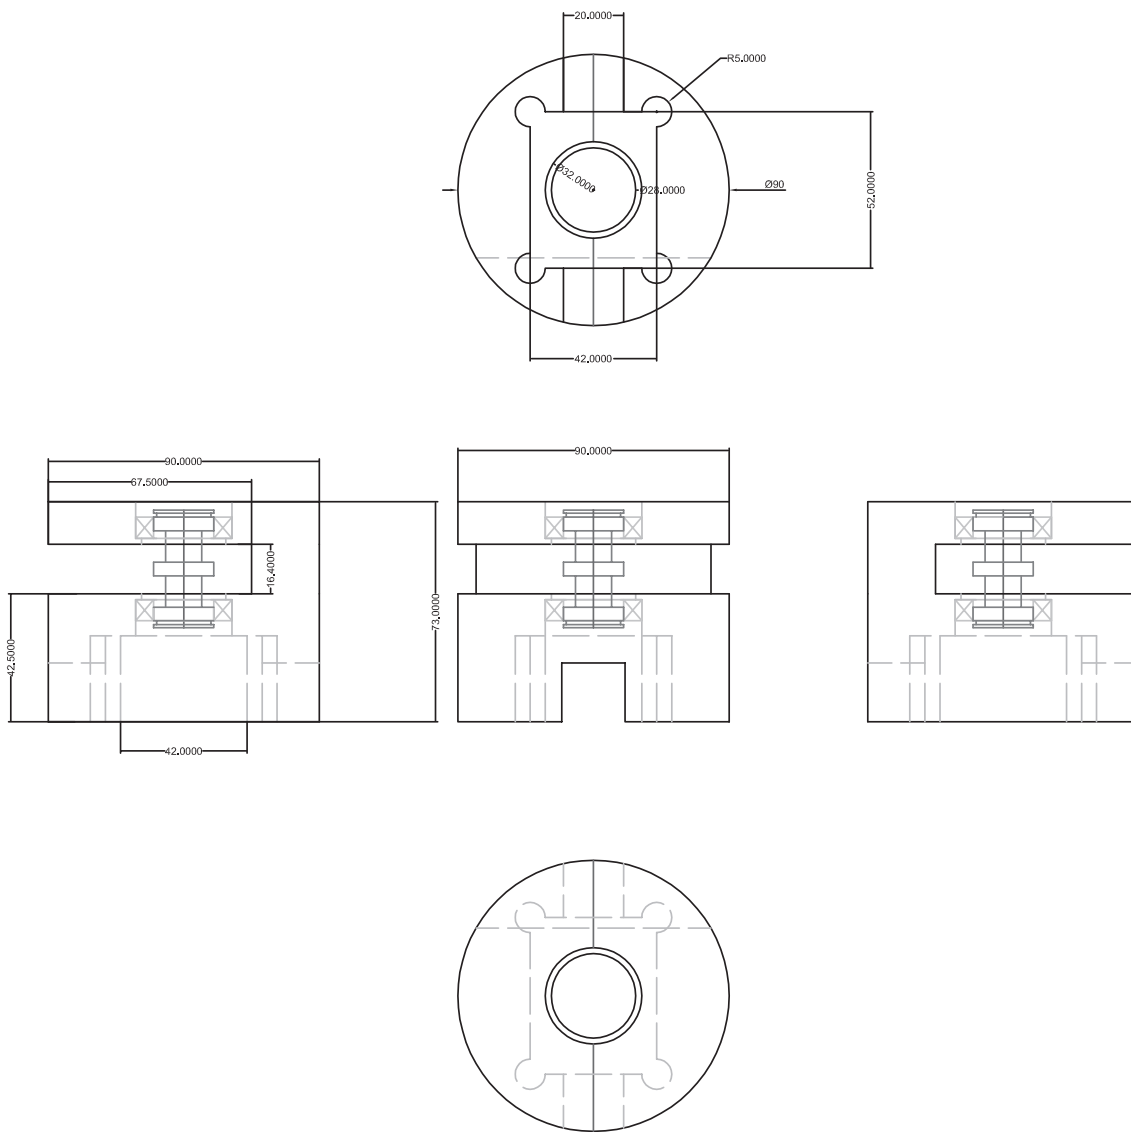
Ensemble coin supérieur+roulement+axe assemblé.
